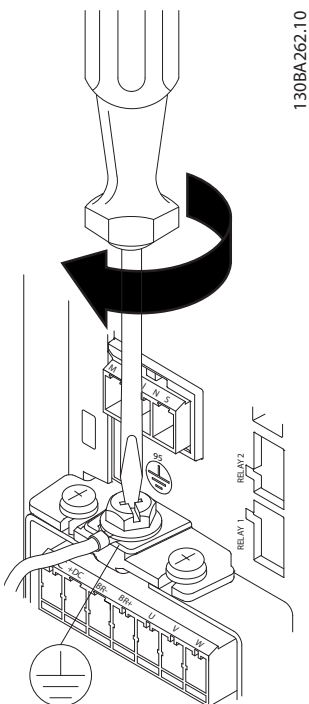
Lors du montage des câbles, monter puis serrer le câble de terre en premier.
